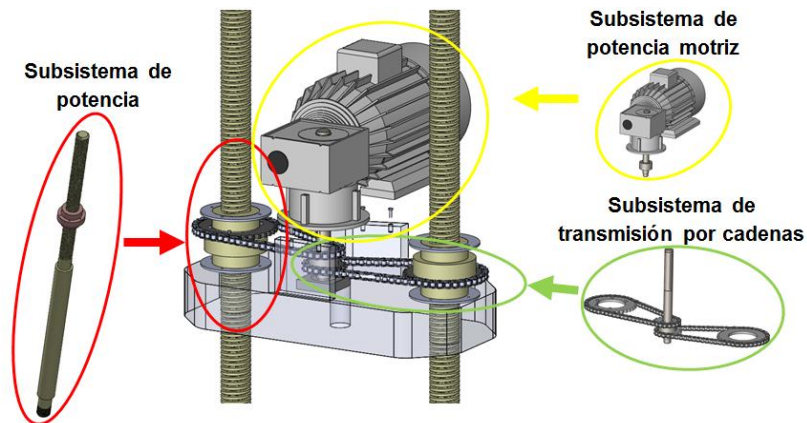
Explosionado del sistema de transmisión de movimiento del yugo superior de la máquina calibradora de fuerza universal.
